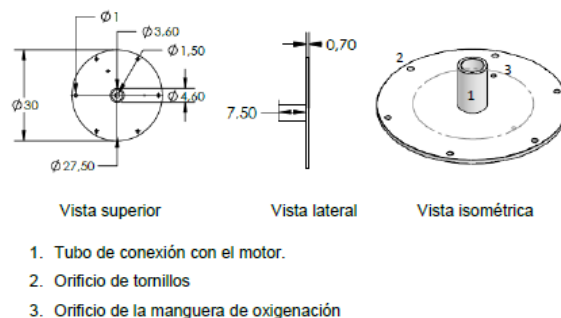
Dimensiones de tapa (Diseño en SolidWorks2017®)
